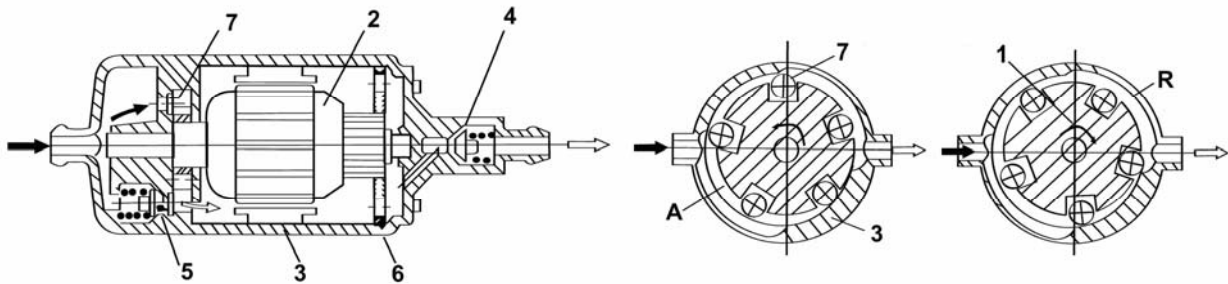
Pompa de alimentare cu combustibil: 1- rotor cu role; 2- motor electric; 3- carcasă pompă; 4- supapă refulare; 5- supapă de reglare a presiunii; 6- placă rigidizare; 7- rolă; A- zonă aspirație; B- zonă refulare
